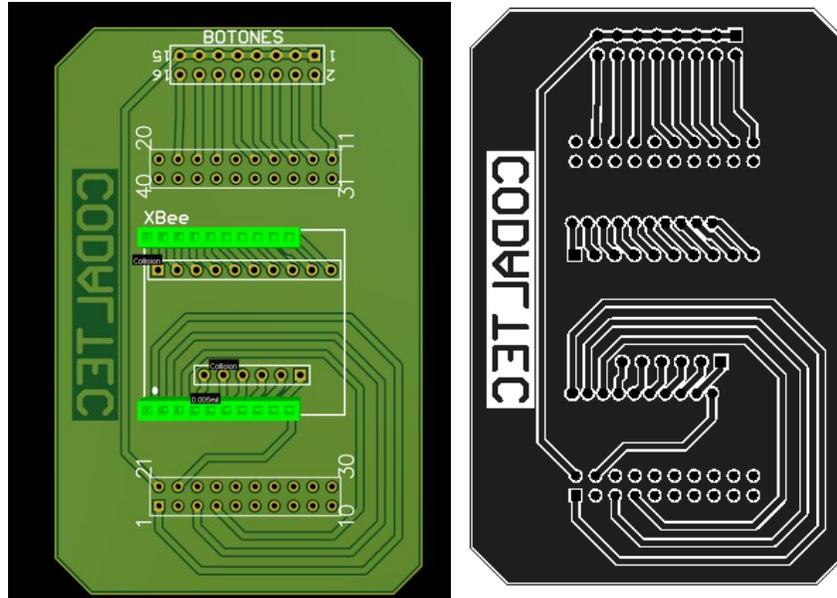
Diseño de la PCB de comunicación - Visual 3D y plantilla para imprimir
